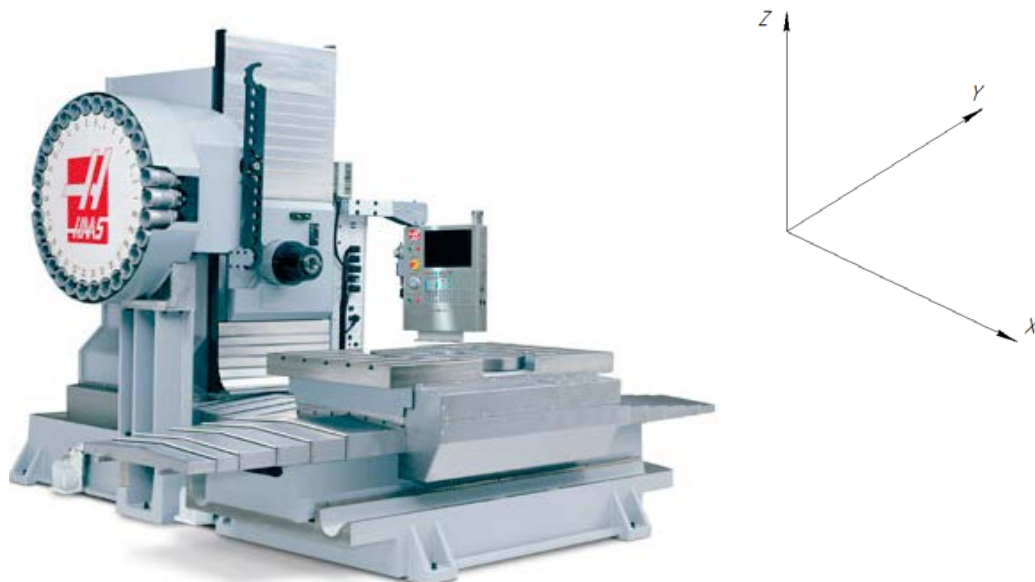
Основные направления движения станка HAAS EC-1600
